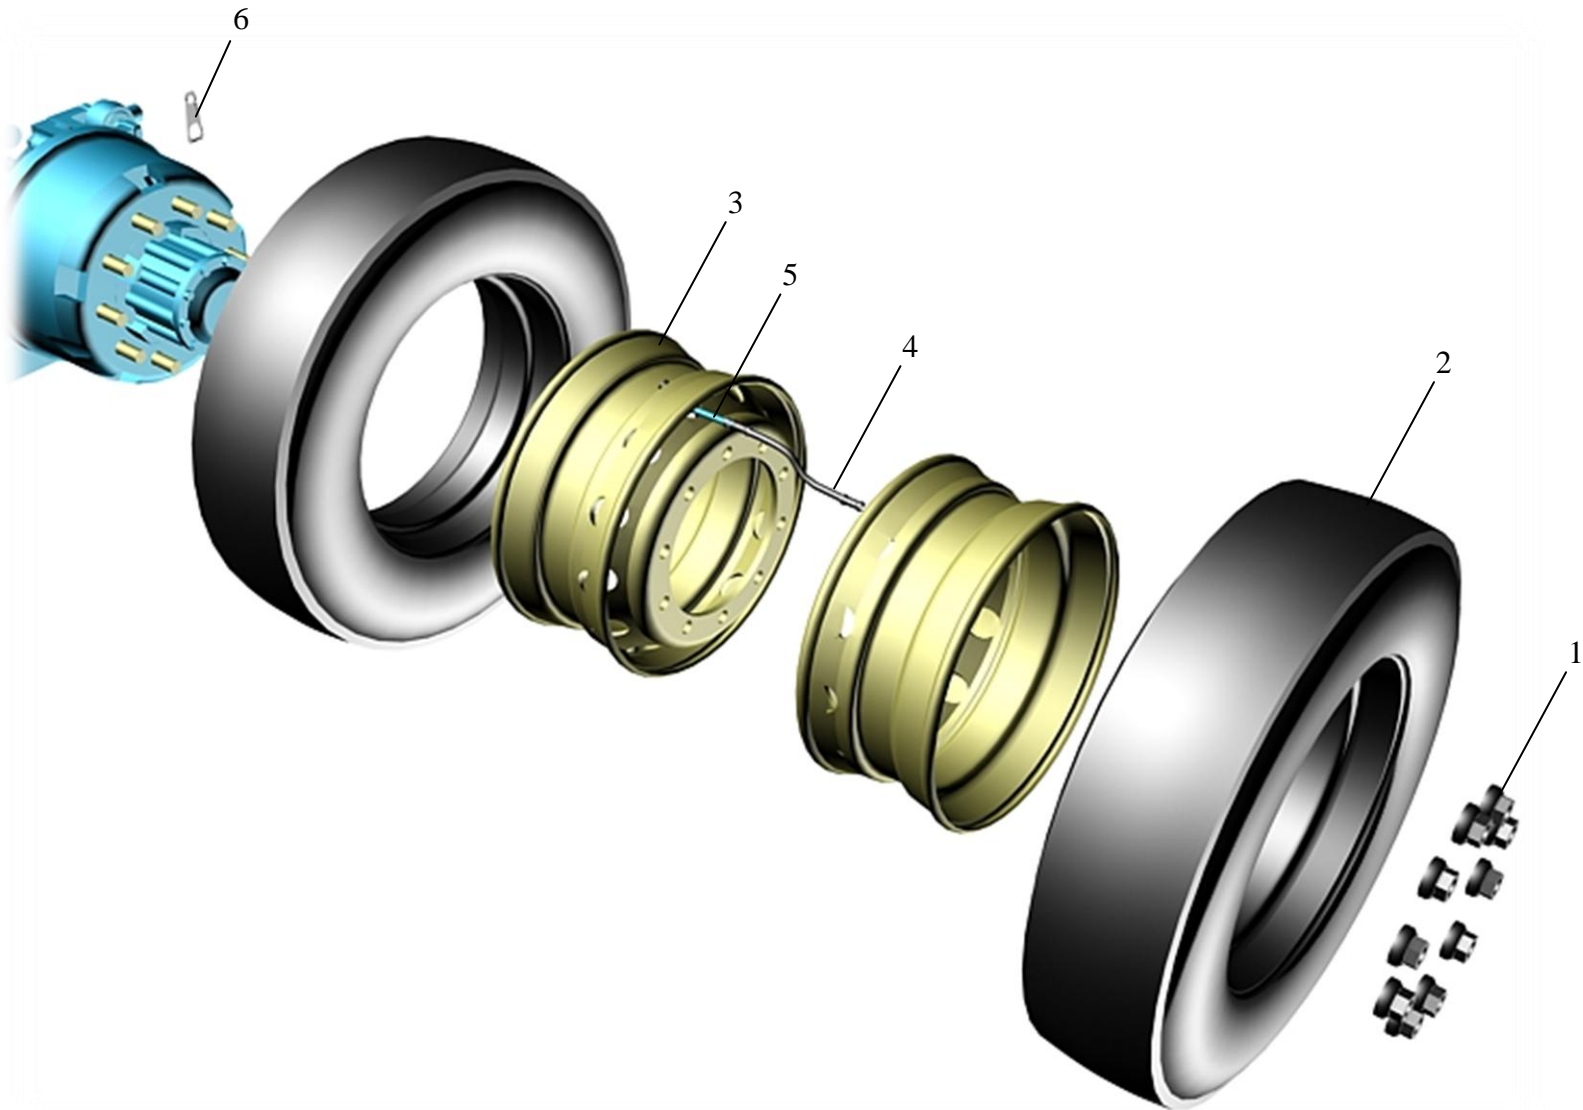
Установка сдвоенных колес АКСМ 32102-210300.000
